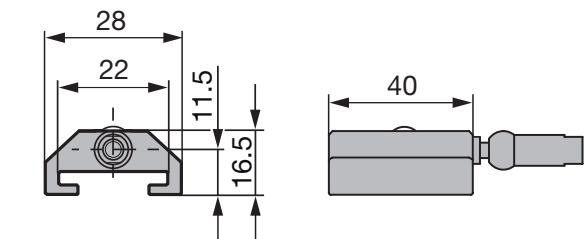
Dimensioni di ingombro datore di posizione BTL5-T-2814-1S
